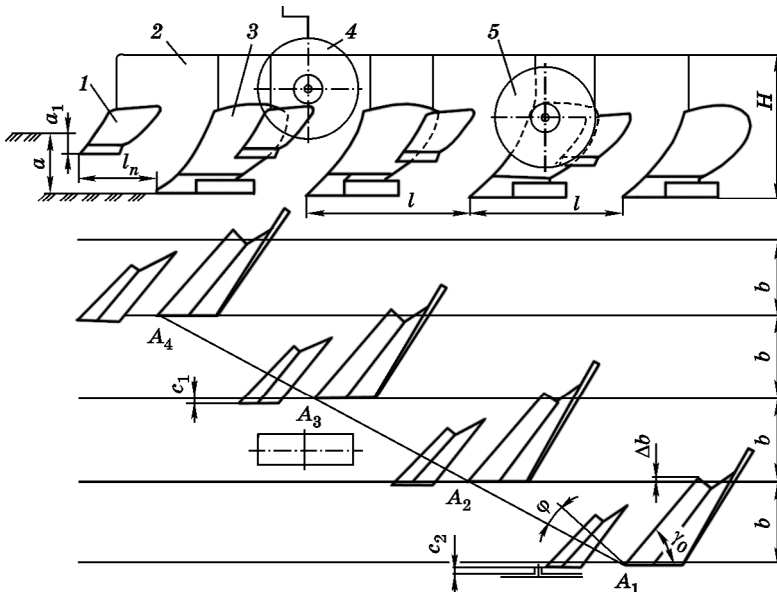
Схема розміщення робочих органів на рамі чотирьохкорпусного навісного плуга:
